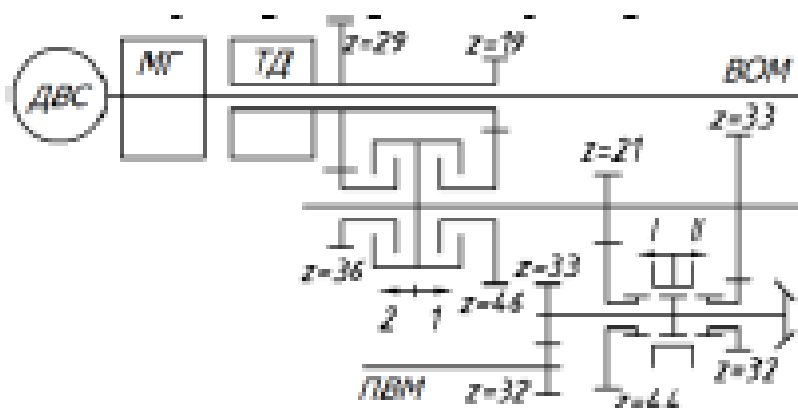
Кінематична схема діапазонного редуктора
